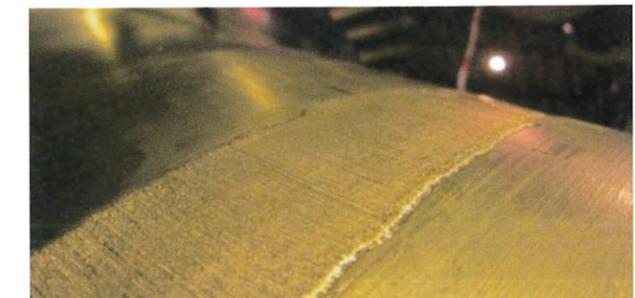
Auftragsschweißgut zum Erneuern der ausgefrästen Schadzone
